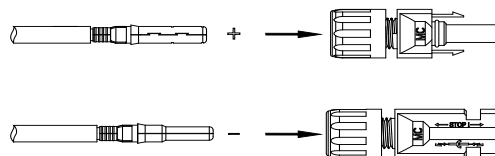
Assemblaggio dei cavi positivo e negativo
